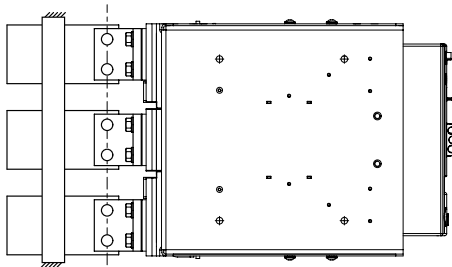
Блокировка выключателя-разъединителя выдвижного исполнения
